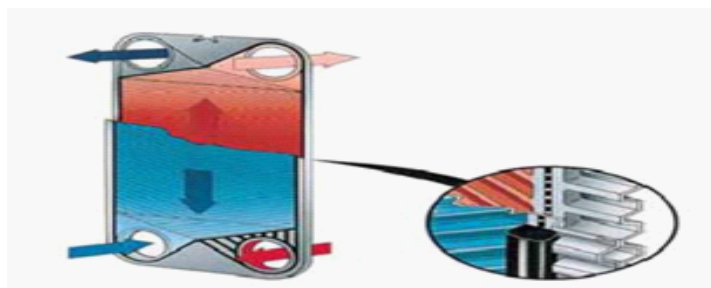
8 : Plaque semi – soudée [25].
